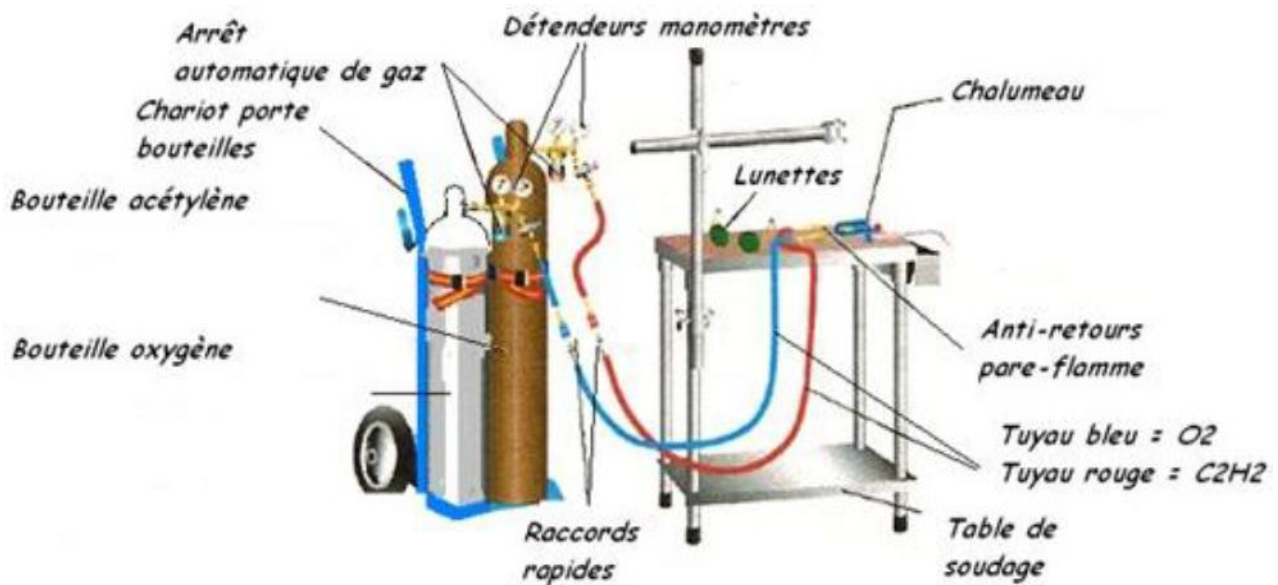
Matériel propre au soudage oxyacétylénique [8].
